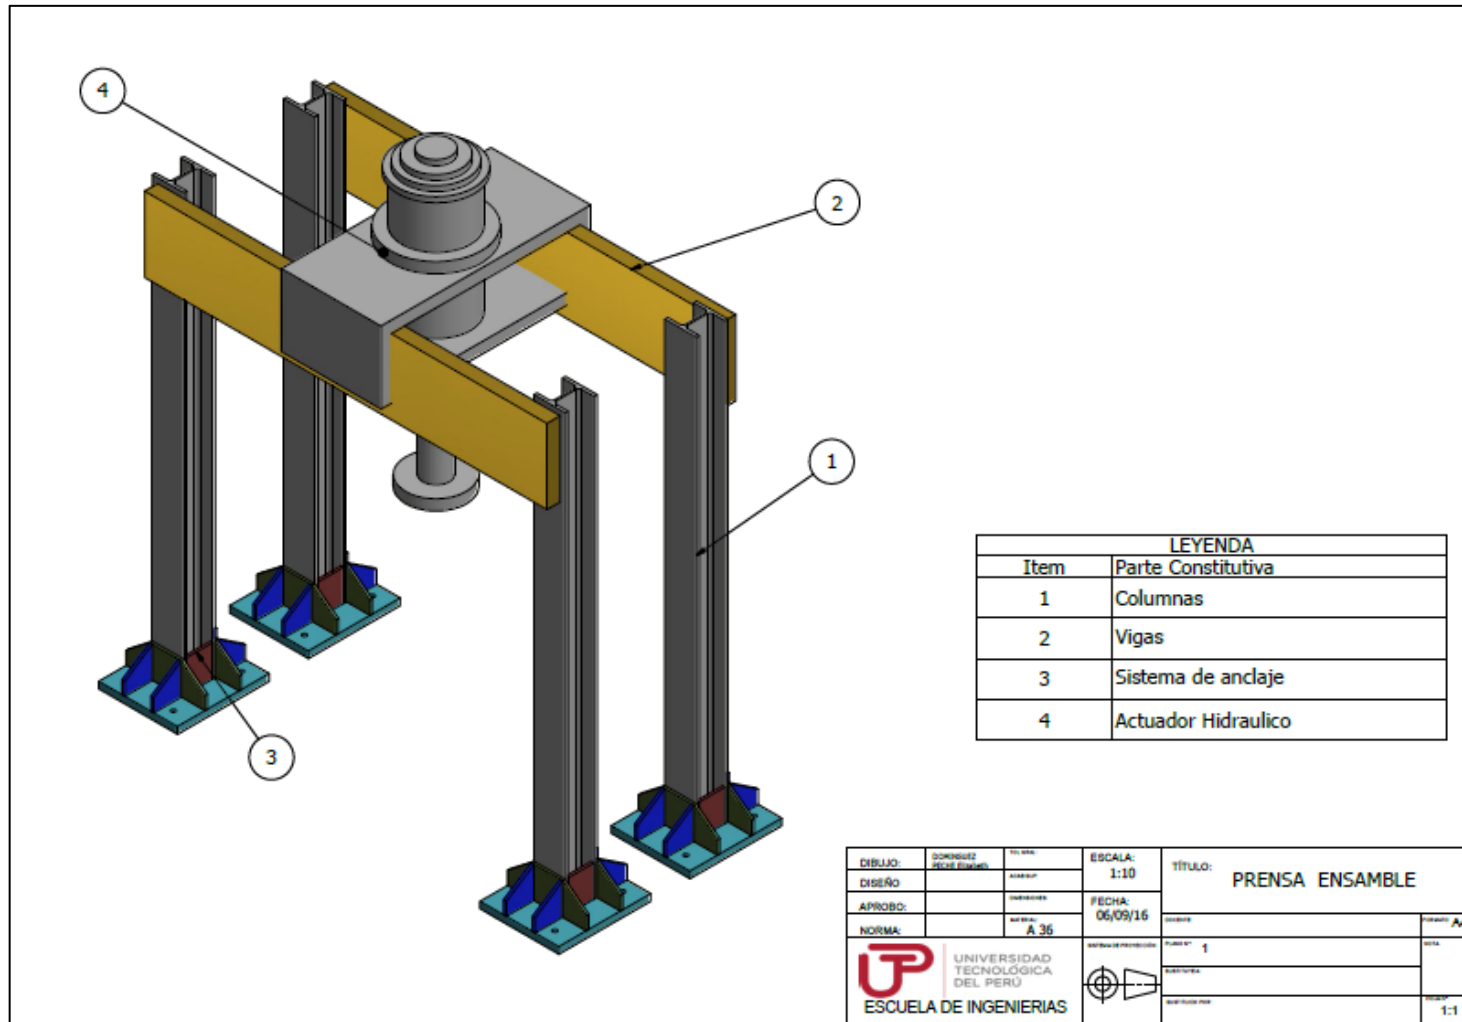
40: Esquema estructural de la prensa hidráulica con las características constructivas sugeridas en la presente tesis. (Elaboración propia, 2 017)
